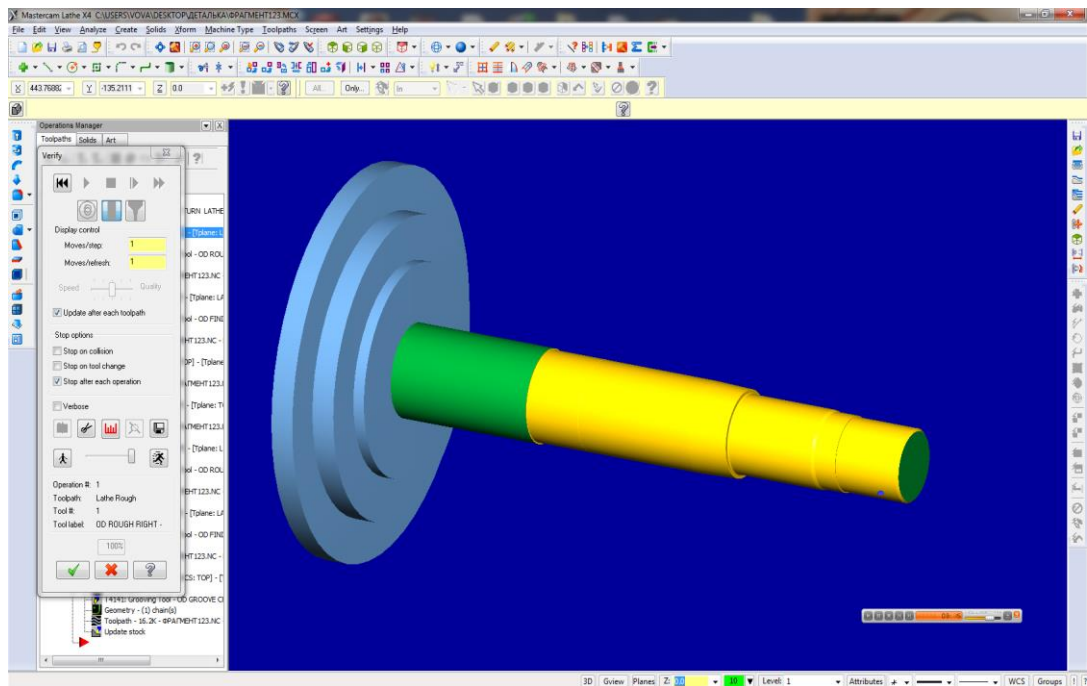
Обробка деталі «Вал» з однієї сторони
